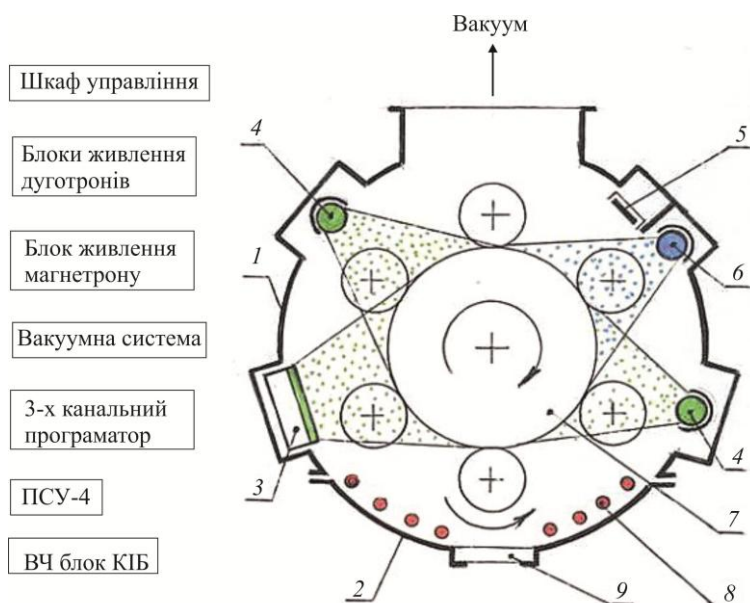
Блок схема модернізованої установки ВУ-700 : 1 – вакуумна камера, 2 – двері; 3 – магнетрон; 4 – дугометр (№ 1, № 3); – 5 – катод тліючого розряду; 6 – дугометр (№ 2); 7 – експонуюча оснастка подвійного планетарного обертання; 8 – електронагрівач; 9 – оглядова система
